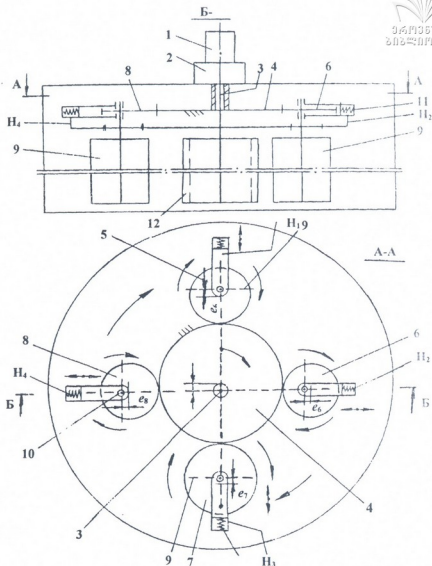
Мешалка с планетарным приводом с эксцентричными цилиндрическими колесами
